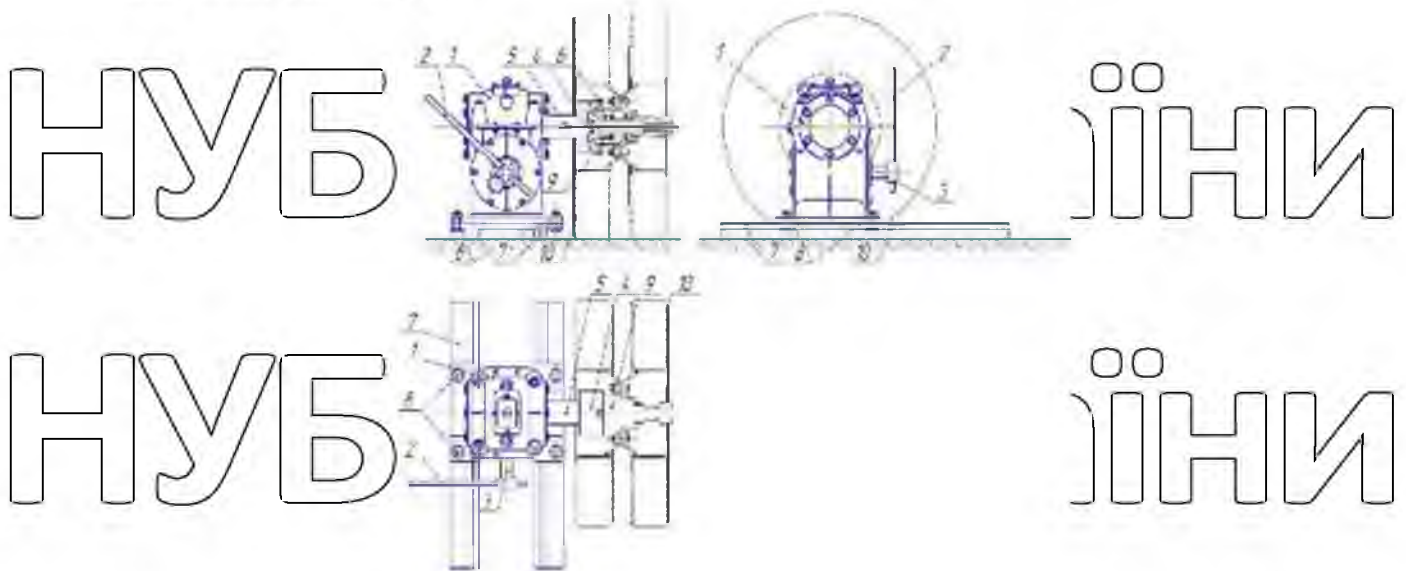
Схема стенда визначення поздовжнього коефіцієнта зчеплення колеса з полотном дороги [67]: 1 – черв'ячний редуктор; 2 – динамометричний ключ; 3 – швидкохідний вал редуктора; 4 – сполучна муфта; 5 – тихохідний вал редуктора; 6 – затискні болти; 7 – пластина; 8 – регулююча по висоті опора; 9 – маточина автомобіля; 10 – колесо.
